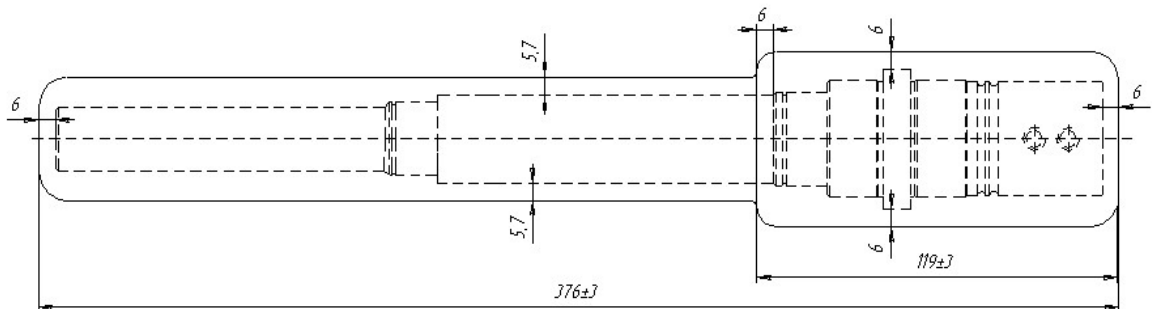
Заготівля шпинделя з нарахованими припусками та допусками
